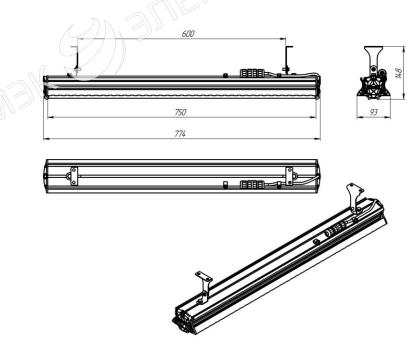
Светильник «L-industry 90 Turbine» с поворотным креплением.
